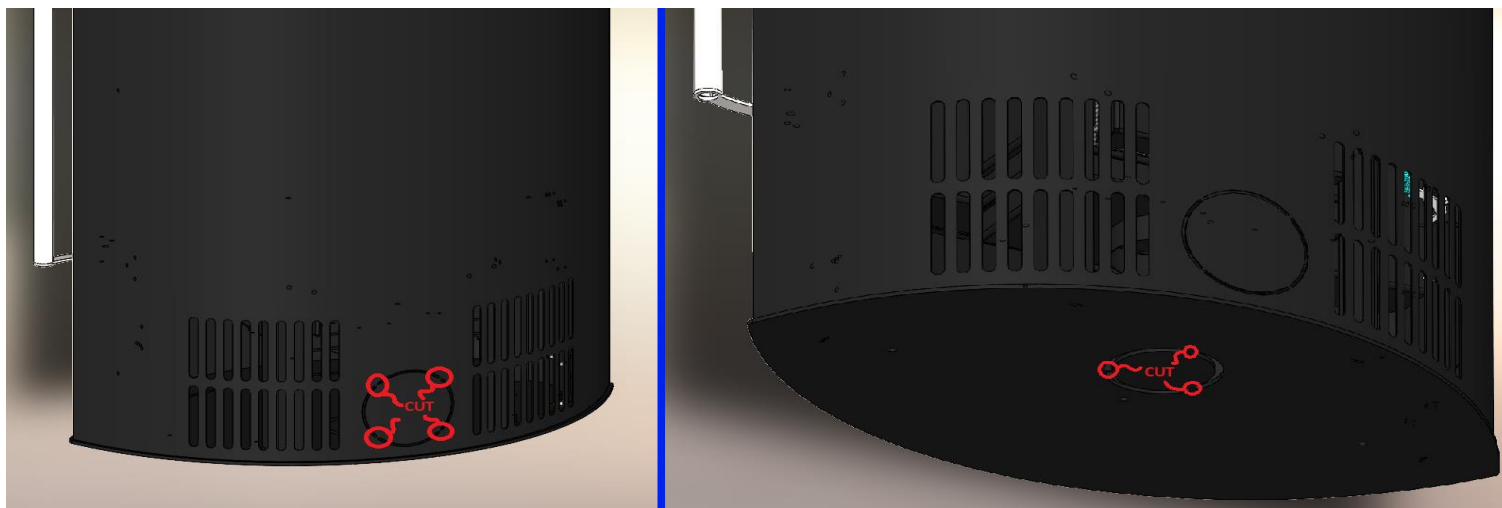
Découpe des micro-joints pour l'arrivée d'air extérieur à l'arrière / au sol
